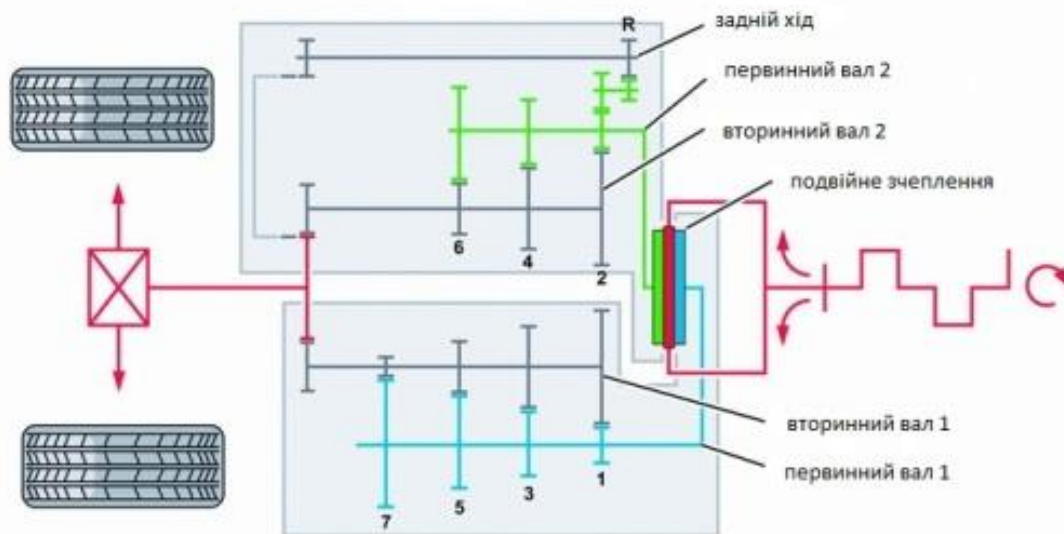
Принципова схема роботизованої коробки перемикання передач з двома зчепленнями
